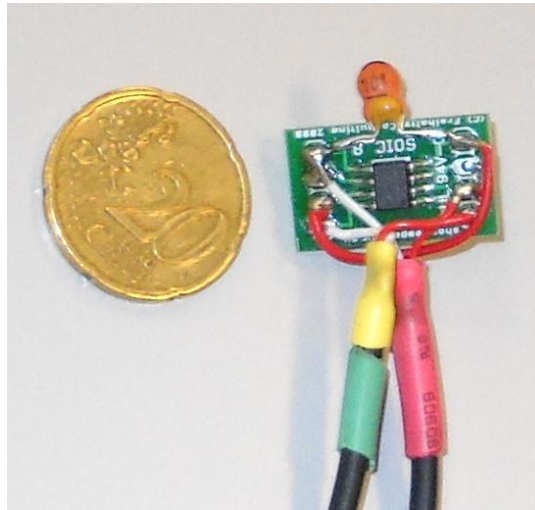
Sensor CSA-1V cableado y soldado sobre placa PCB.
